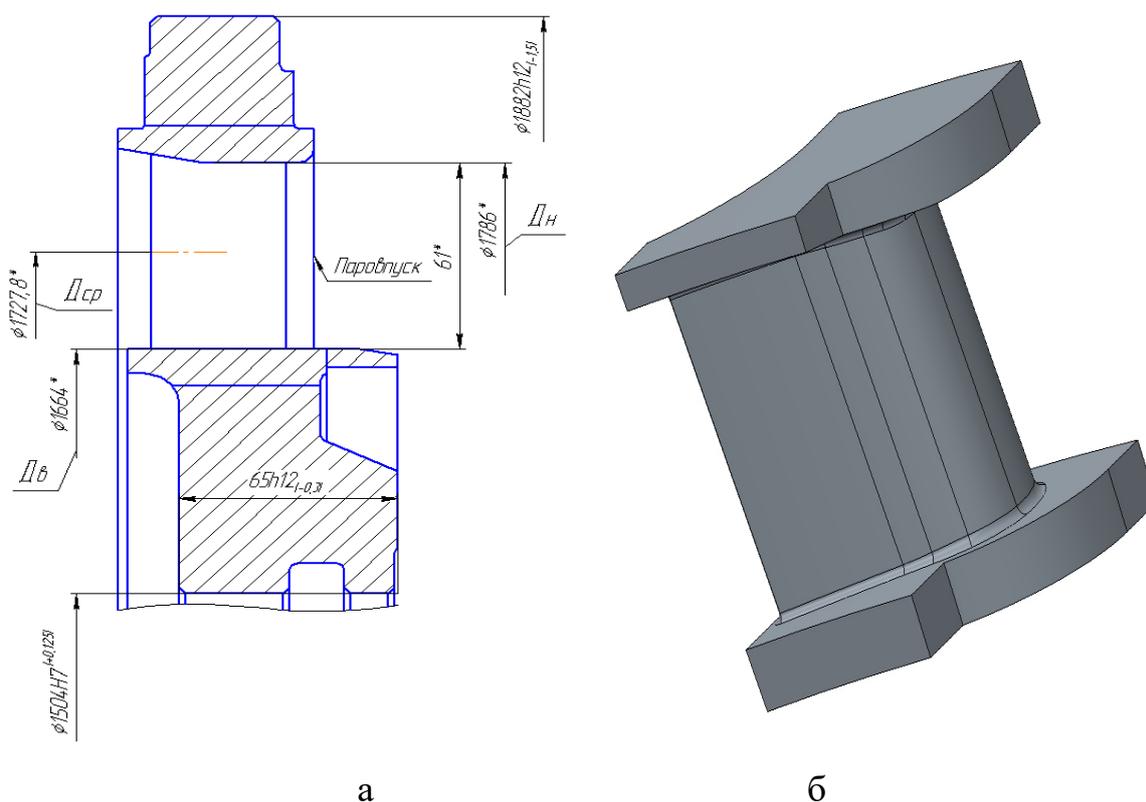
а – диафрагма с цельнофрезерованными бандажами;
